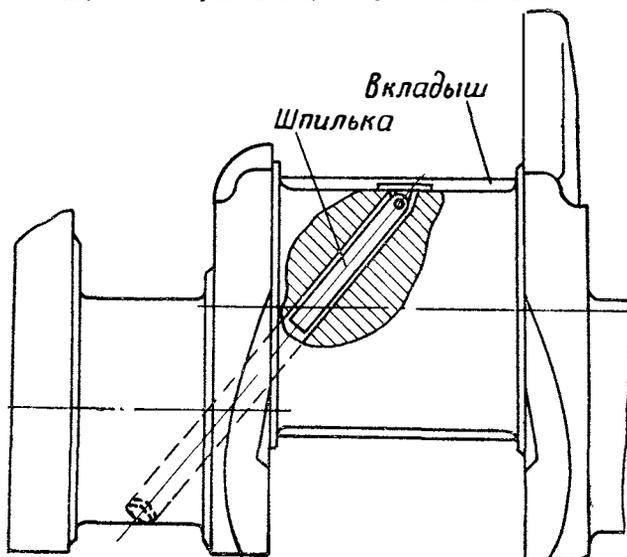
Установка шпильки в отверстие коренной шейки коленчатого вала
